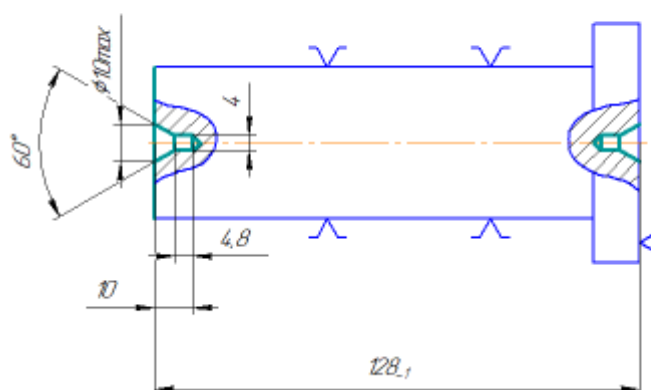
Эскиз 005 фрезерно-центровальной операции
